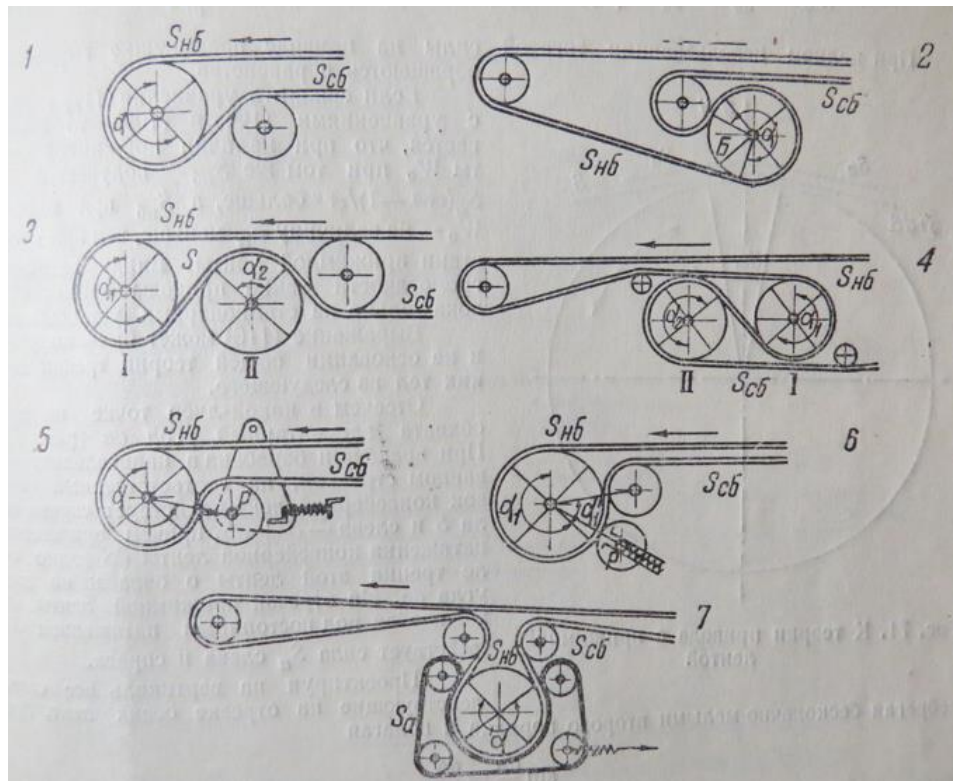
Схеми приводу стрічкового конвеєра:
